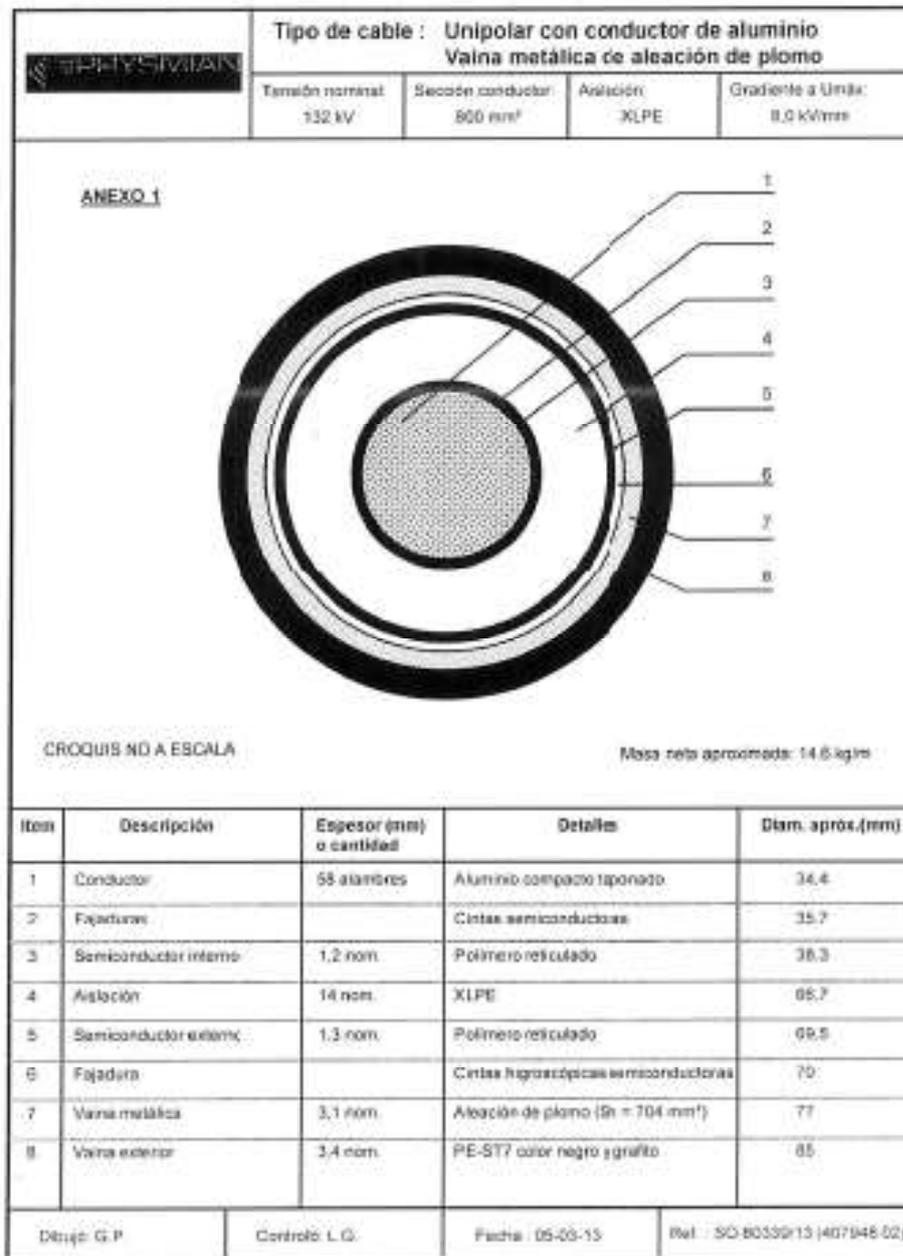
Características del cable utilizado para las ternas ternas en 132 kV a instalarse.
